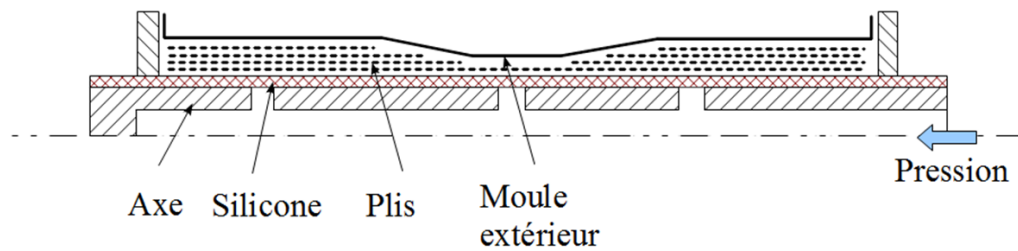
Dispositif de moulage pour les éprouvettes tubes
